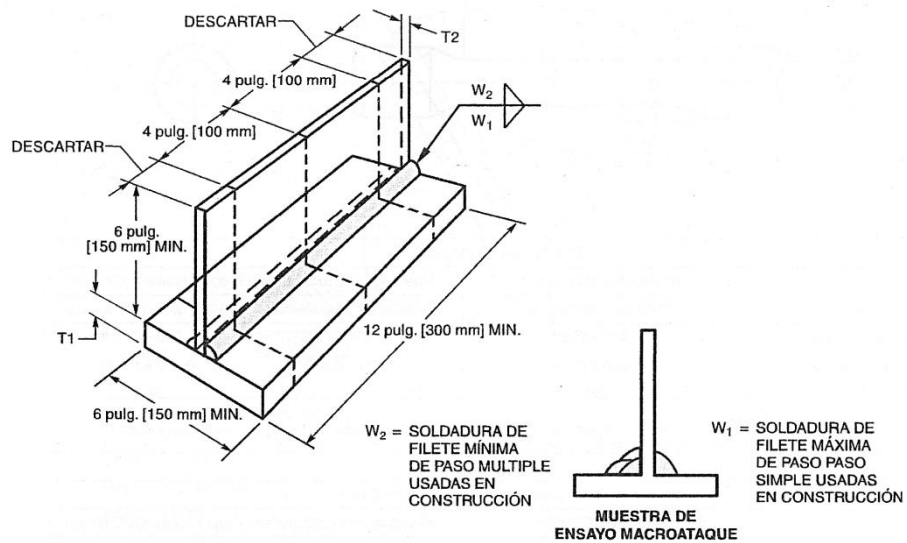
Ensayos de sanidad de soldadura de filete para WPS.
